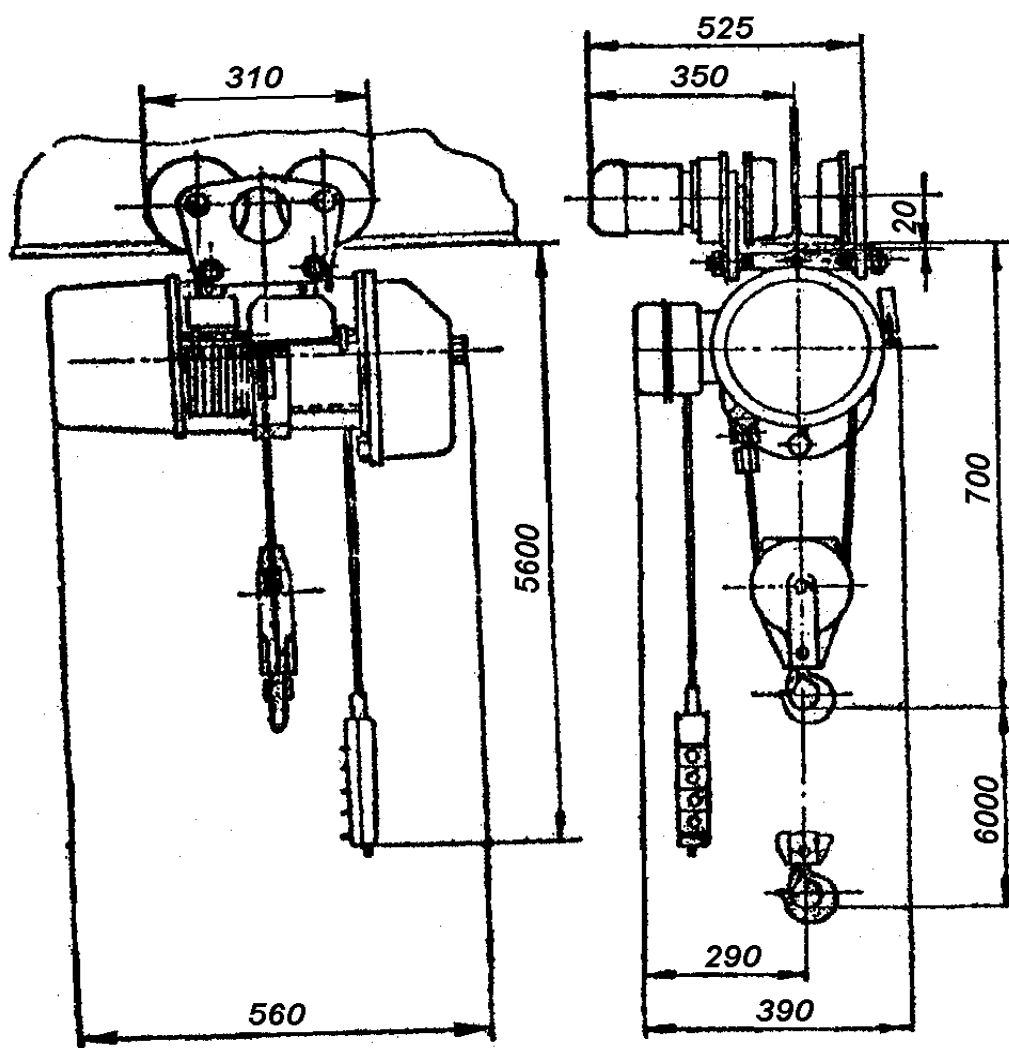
Общий вид и габаритные размеры электроталей ТЭ050-511
